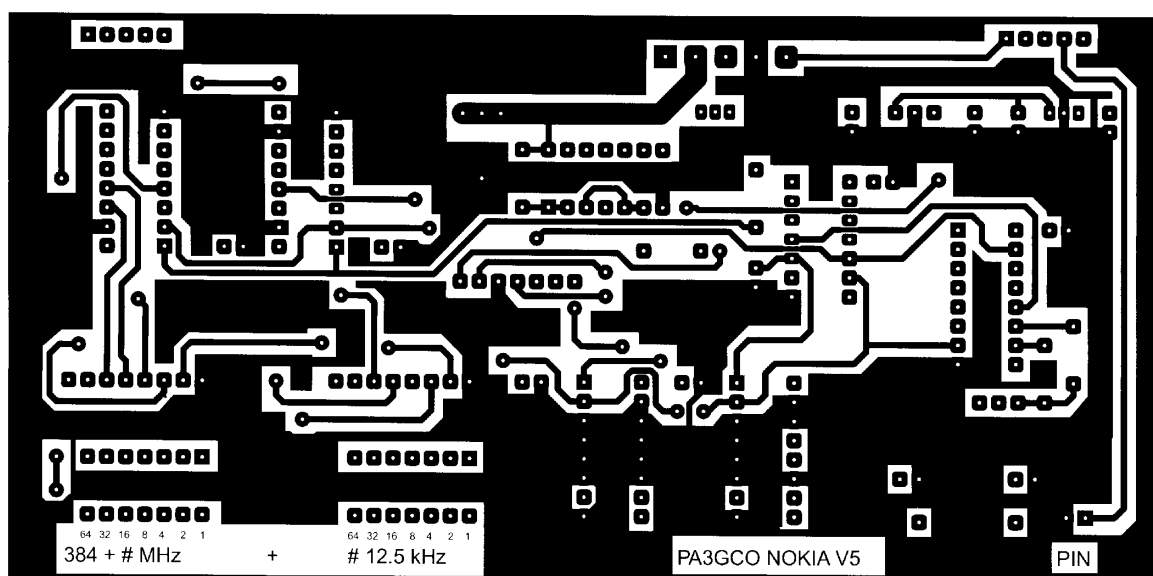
De layout van de bovenzijde gezien, afm. print 75 x 153 mm.
